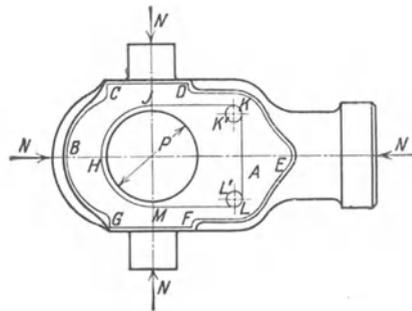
Schmiedestück zum Kreuzkopfkörper.
